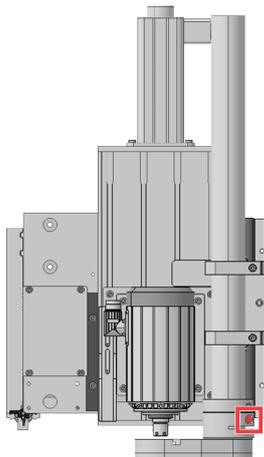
LÖSEN DER SCHRAUBE DES SAUGSCHUHS
